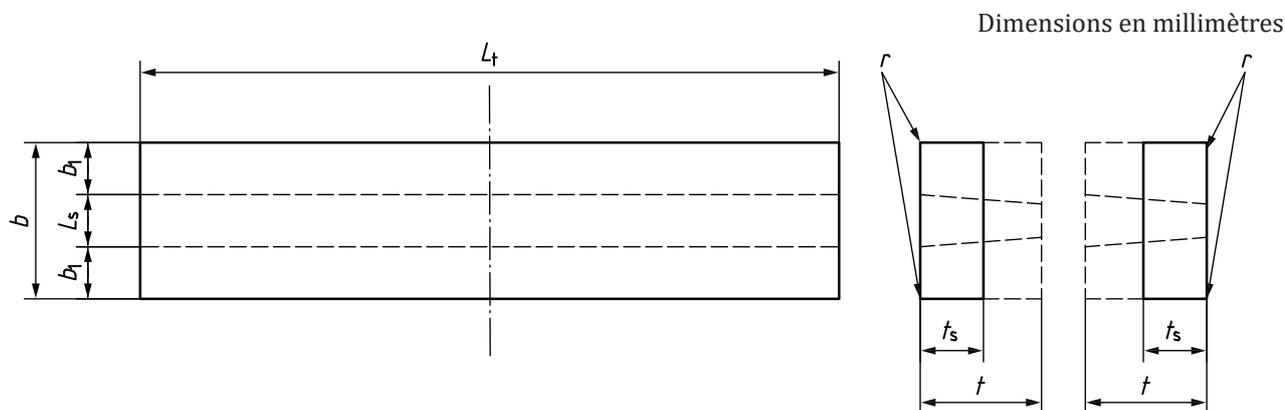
Éprouvette de pliage transversal de côté sur soudure bout à bout (TSBB)
